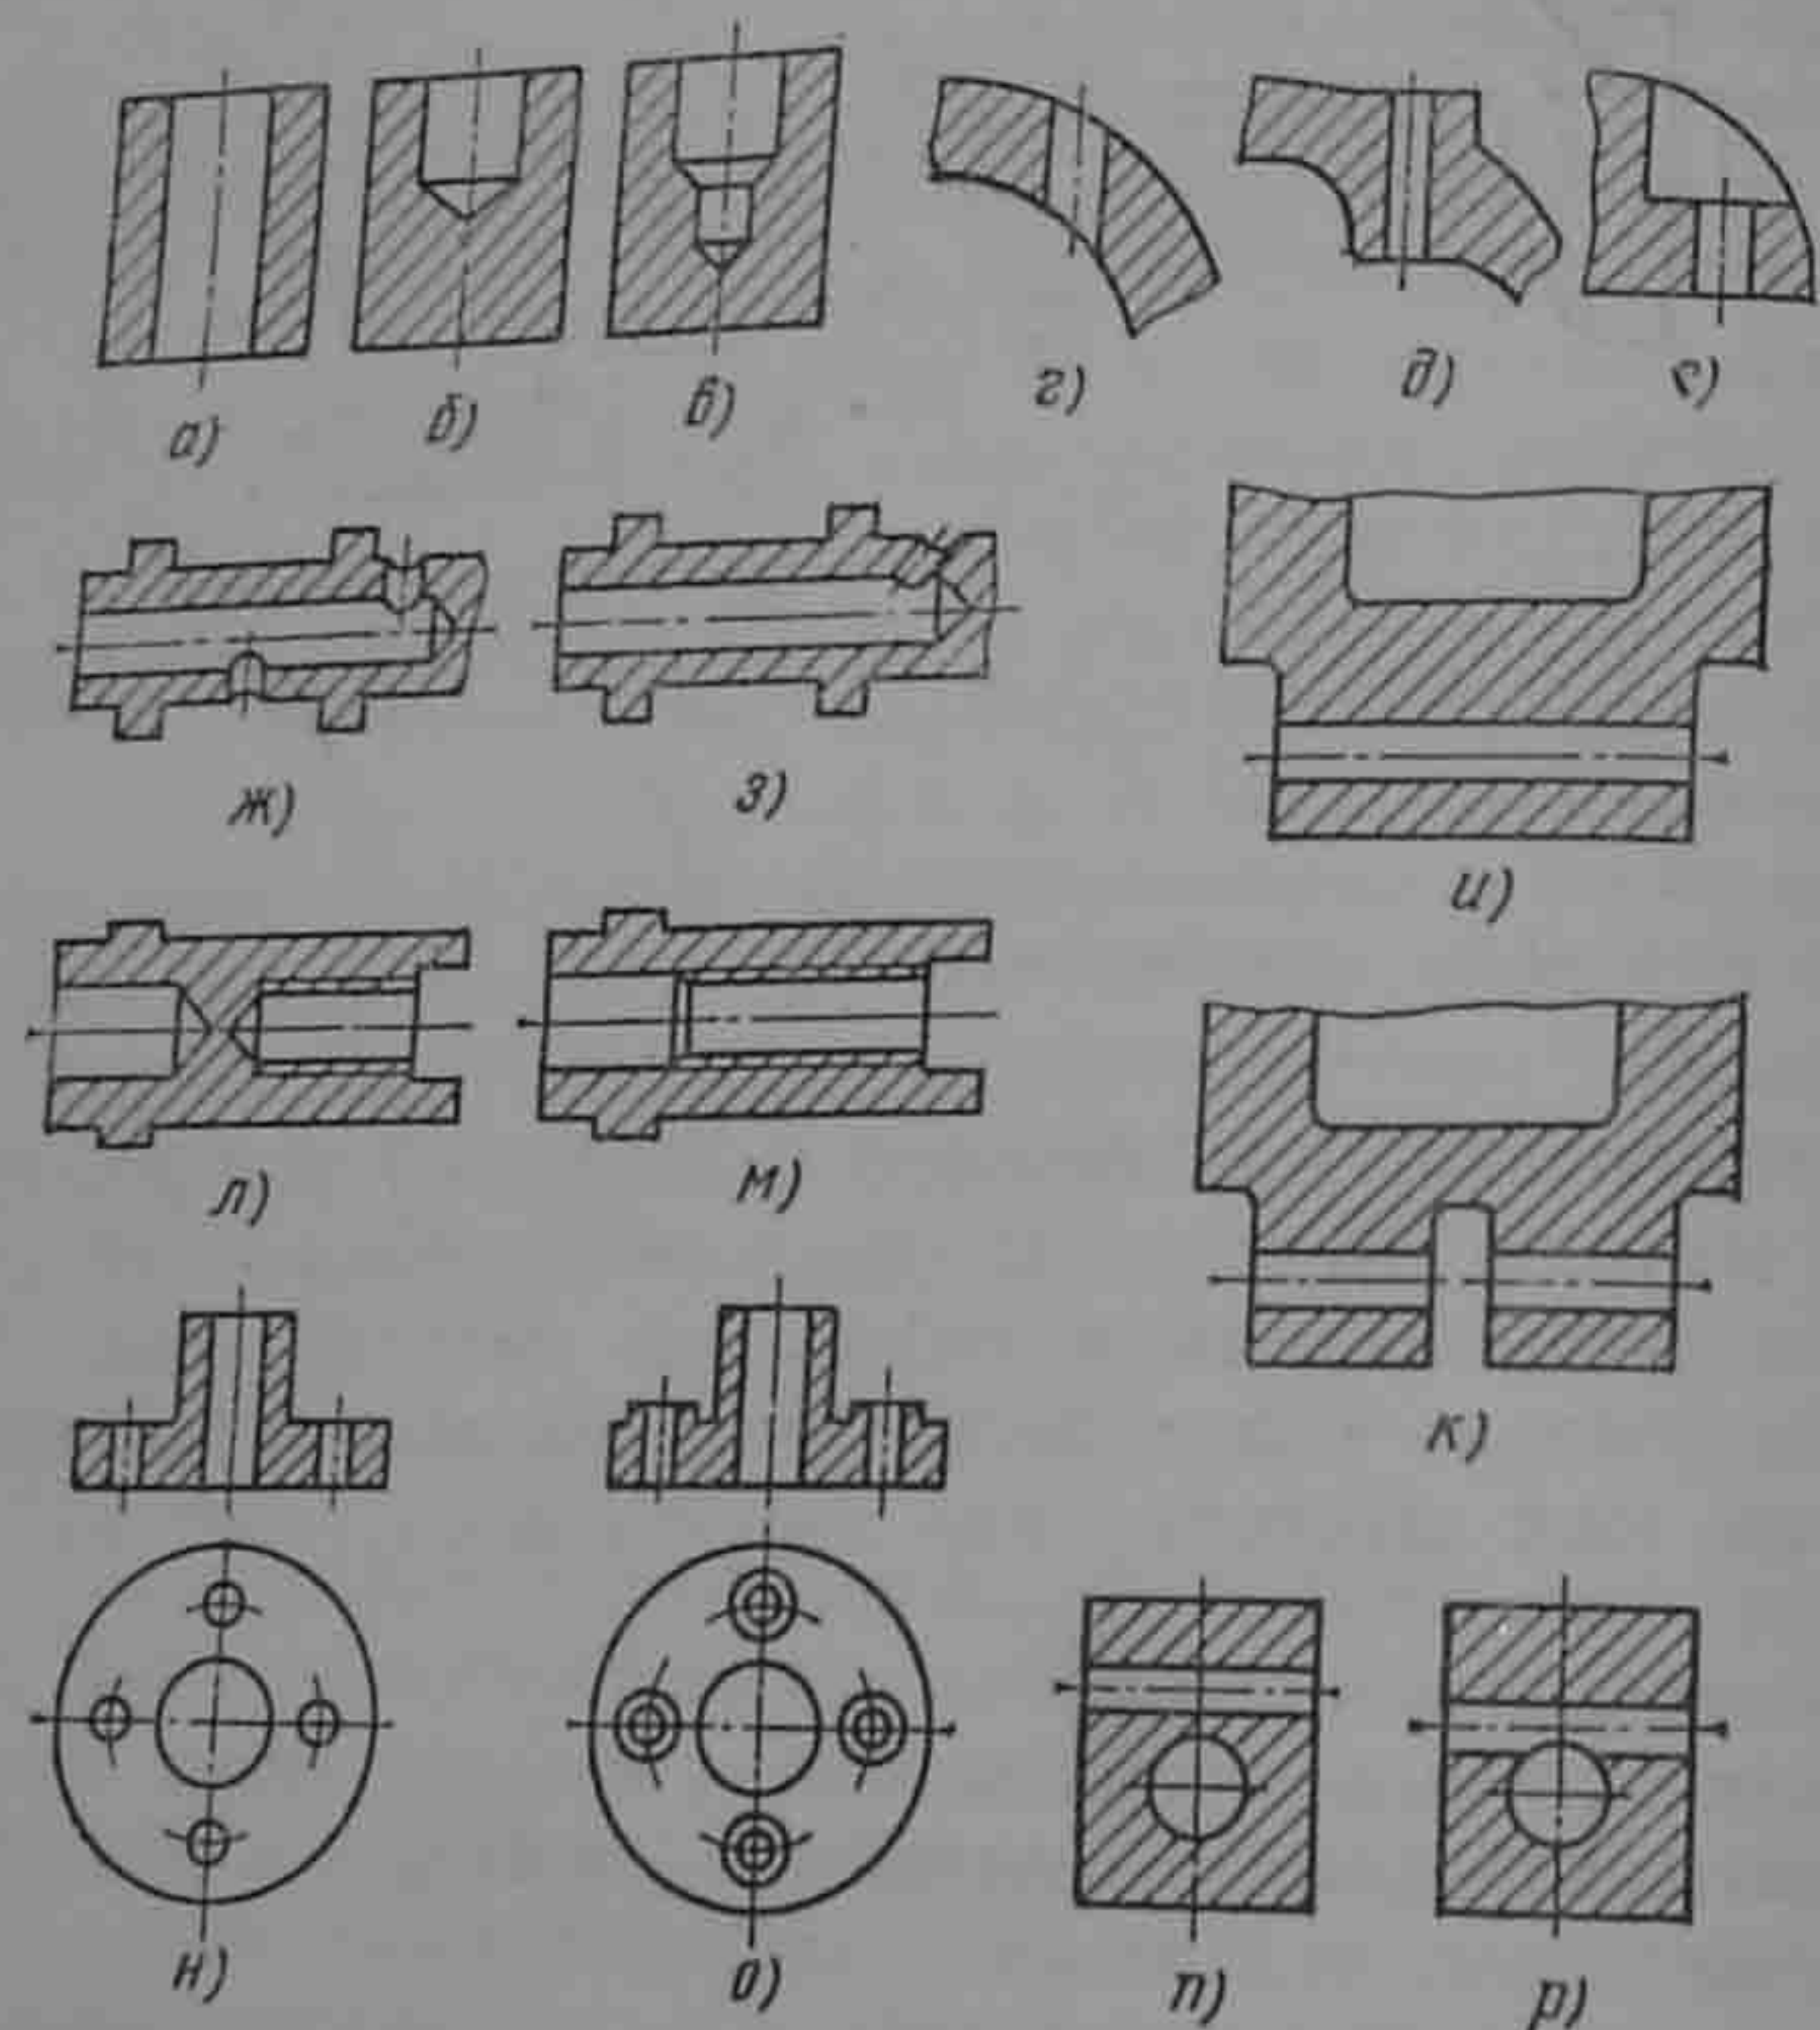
Примеры конструкций деталей машин, обрабатываемых на сверлильных станках
